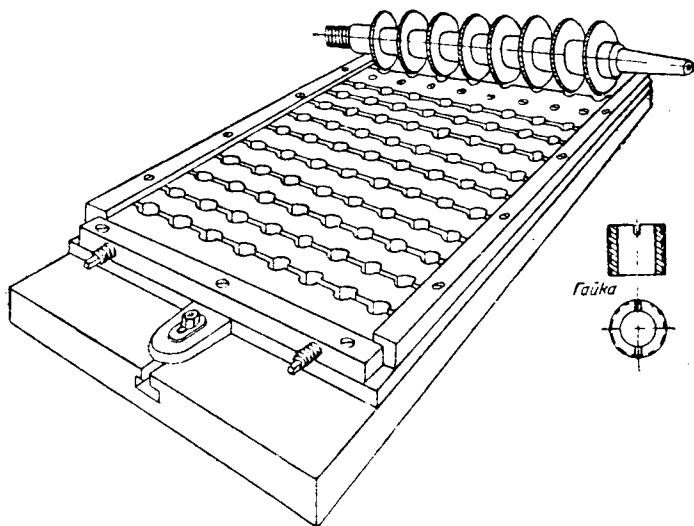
Многоместное приспособление для одновременного крепления 20 деталей
